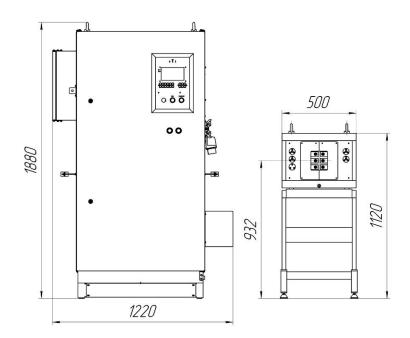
Габаритный чертёж. Установка индукционная нагревательная ПЕТРА-0501
